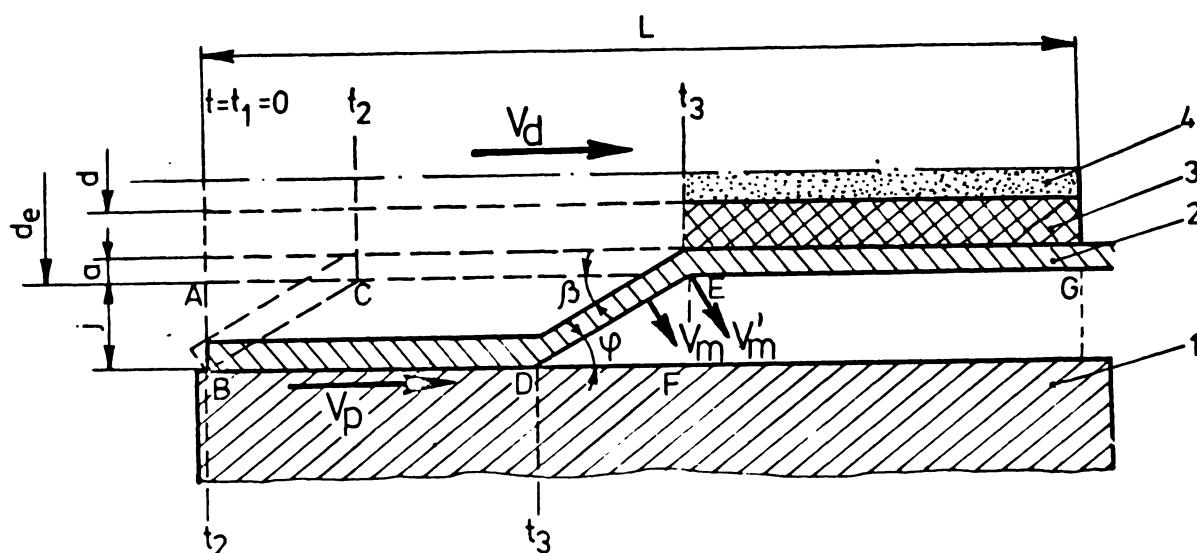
Mecanismul mandrinării prin explozie a țevilor la placă tubulară
